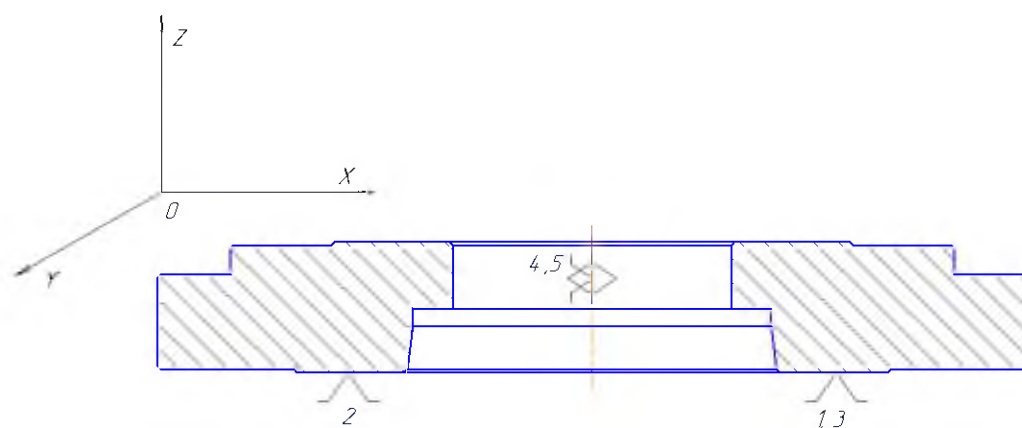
Схема базування при механічній обробці правого торця фланця, внутрішнього отвору та торцевого уступу
